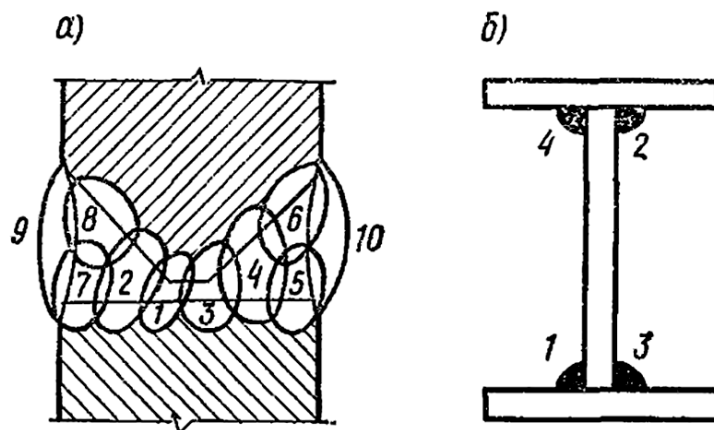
Чередование швов: а — при сварке двустороннего шва; б - при сварке поясных швов балки; 1-10- последовательность швов.
